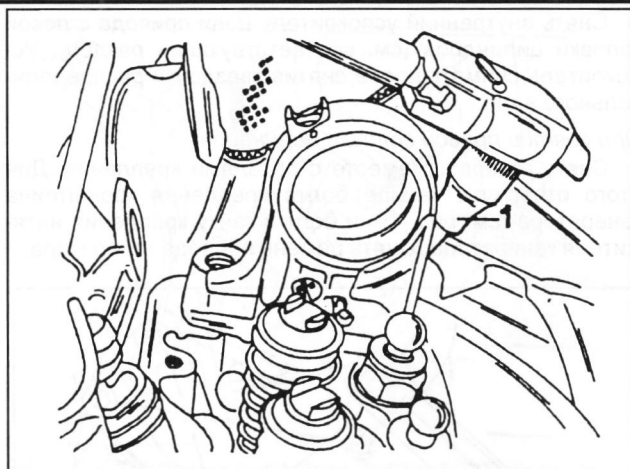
Отворачивание болтов крепления головки цилиндров.
